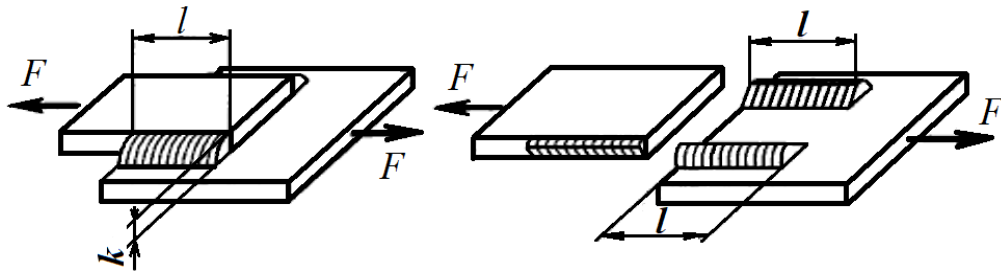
Схема нагружения фланговых угловых сварных швов силой F
